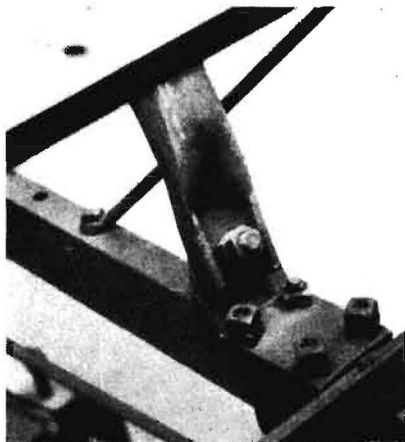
Einpressung eines Rohres als Sitz für eine Befestigungsschraube. Gute Kräfteinleitung
